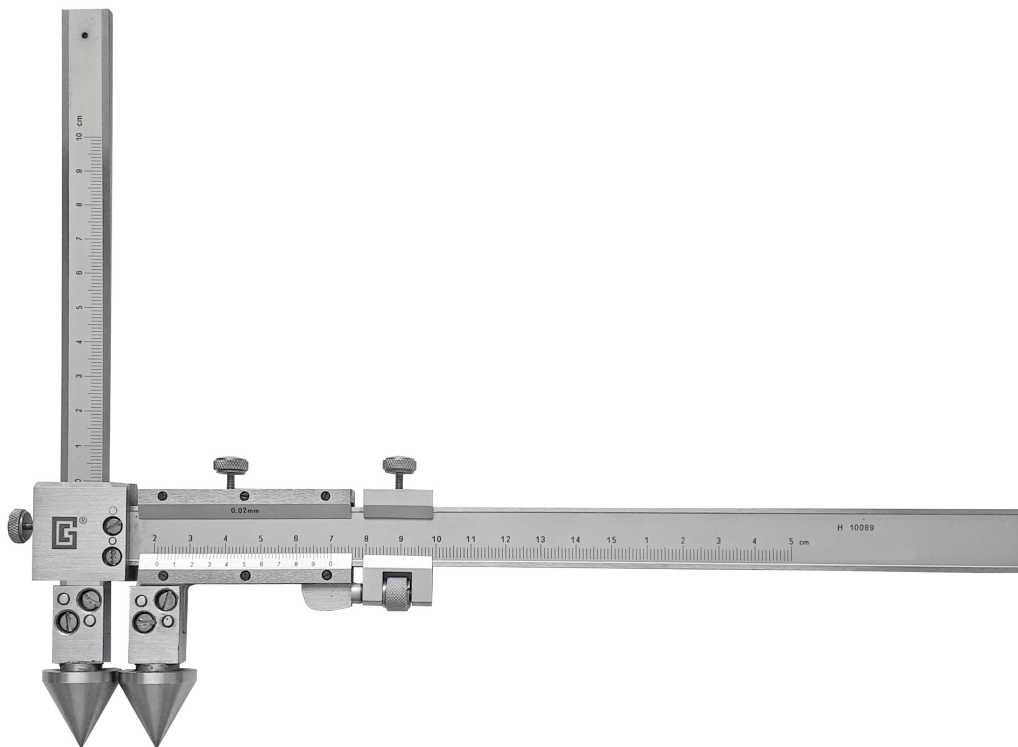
Общий вид штангенциркулей модели ШЦС-127
